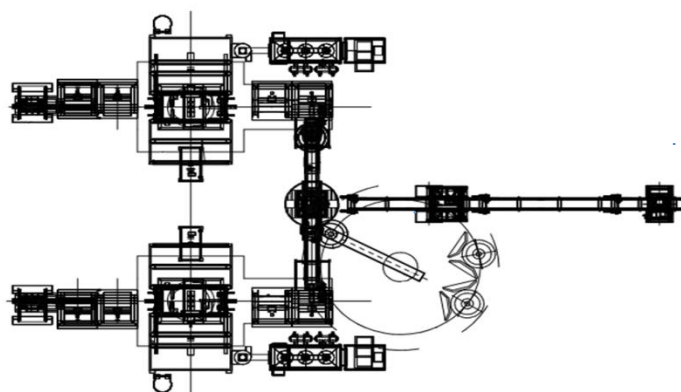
Схема расположения оборудования автоматической установки для дробеметного упрочнения
